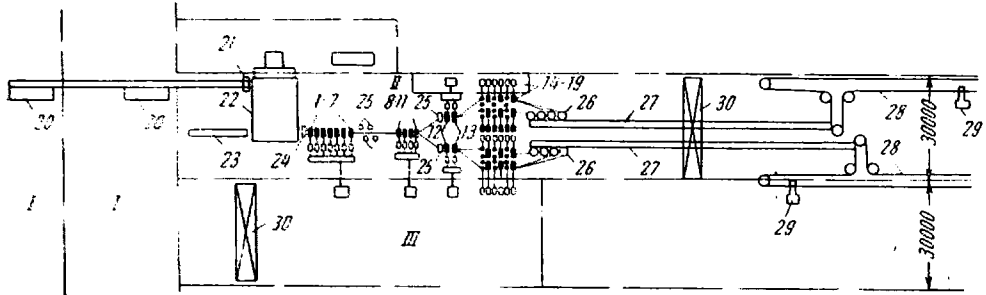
Схема расположения оборудования непрерывного проволочного стана: I — склад заготовок; II — пролет стана; III — машинный зал; 1—7 — черновые клетки первой группы; 8—11 — черновые клетки второй группы; 12, 13 — предчистовые клетки; 14—19 — чистовые клетки; 20 — загрузочные решетки; 21 — вталкиватель; 22 — нагревательная печь; 23 — выталкиватель; 24 — ножницы; 25 — летучие ножницы; 26 — моталки; 27 — муфельные транспортеры; 28 — крюковой конвейер; 29 — пакетирующая машина; 30 — кран 20/5 т
